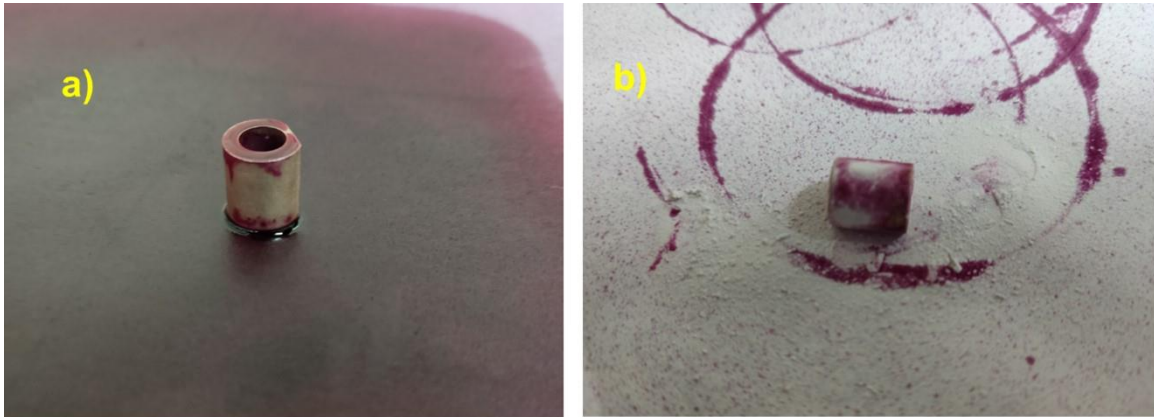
Líquidos penetrantes a) Limpieza b) Revelador
